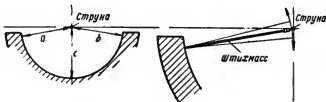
Проверка подшипников относительно оси агрегата.
